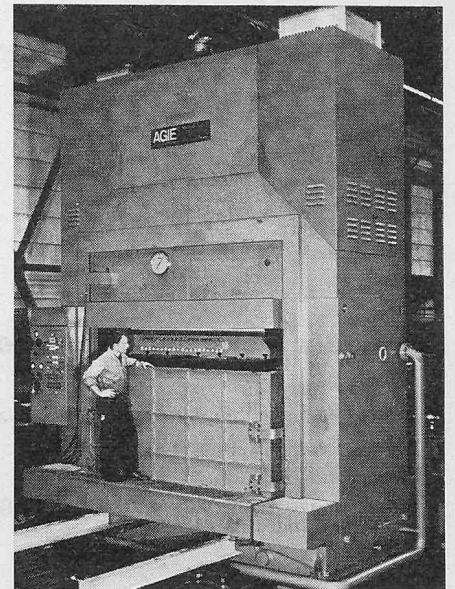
(rechts). Grosserosionsmaschine für die Bearbeitung von Karosseriegesenken. Tischfläche 1600 x 2700 mm; Leistung 12 cm<sup>3</sup>/min; Anschlusswert 125 kVA
